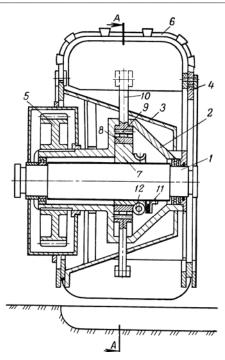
Рабочий орган роторного экскаватора с изменяющимся углом резания грунта: I — неподвижная ось; 2 — ступица; 3 — разгрузочный конус; 4 — обод; 5 — зубчатое колесо привода; 6 — ковши; 7 — эксцентриковая втулка; 8 — обойма с пальцами 9; 10 — тяги; 11 — кронштейн с закрепленным малогабаритным приводом; 12 — малогабаритный привод
